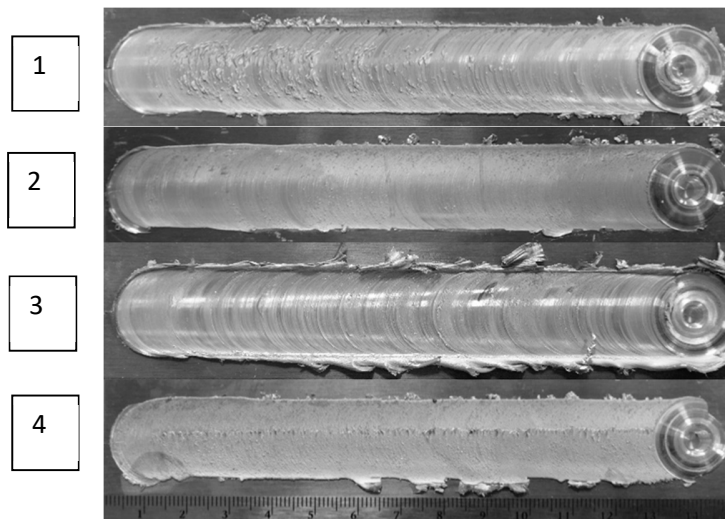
Cordones de soldadura obtenidos mediante FSW. De arriba abajo 90 mm/min – 1085 RPM, 127 mm/min – 1400 RPM, 45 mm/min – 1085 RPM y 187 mm/min – 1400 RPM.
